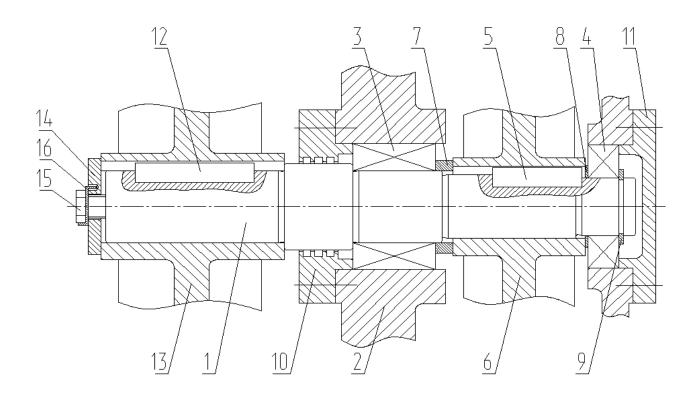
Фрагмент узла мотор-редуктора
